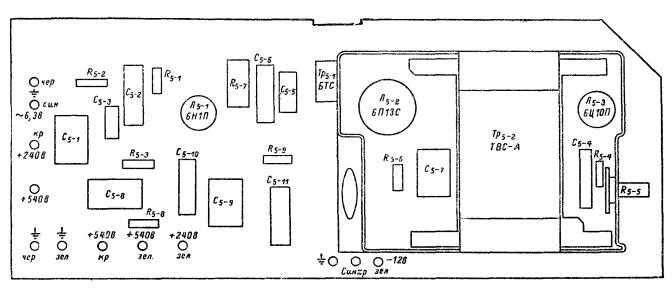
Расположение деталей на плате строчной развертки телевизора «Нева».
